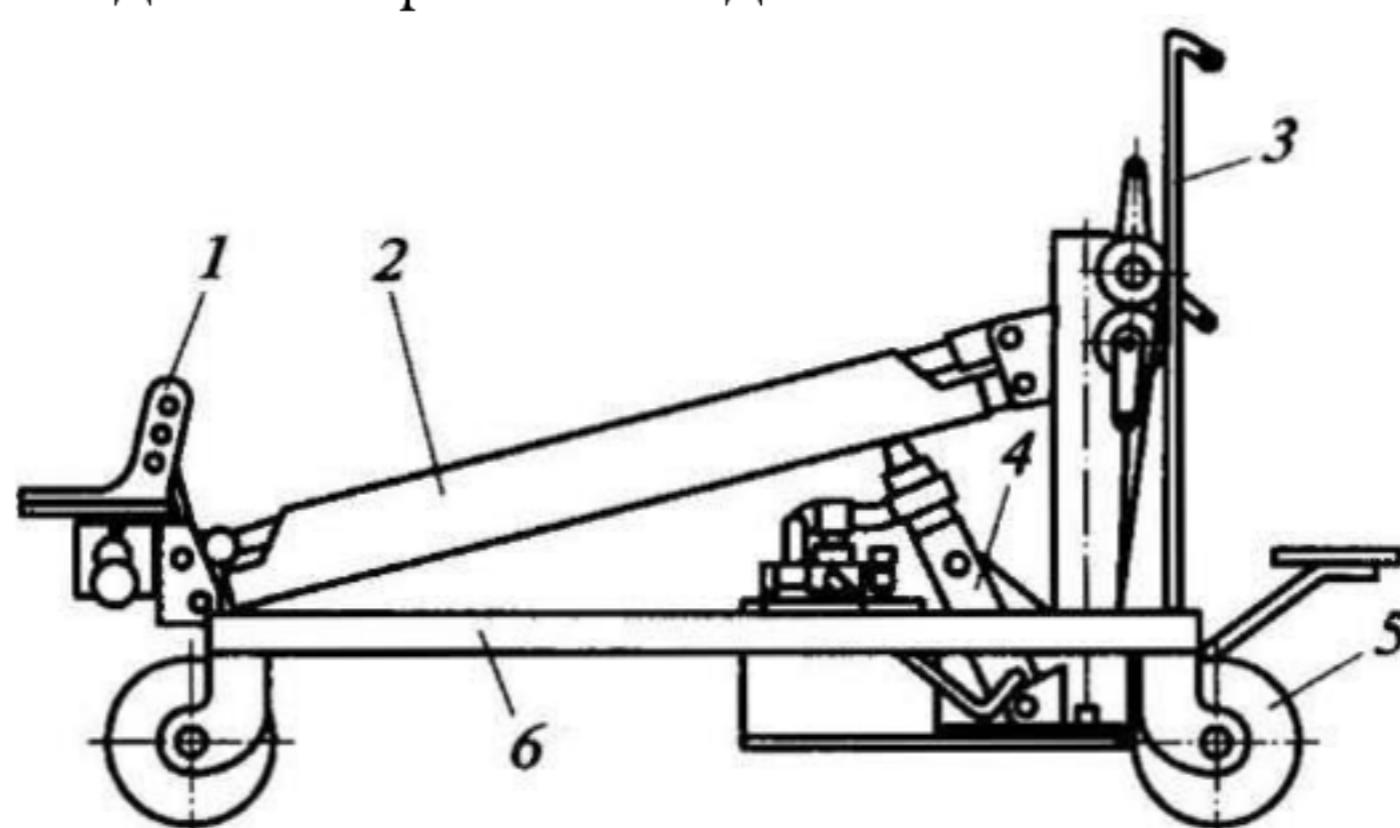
Техническая схема снятия и постановки рессор: 1 — подхват для рессор; 2 — стрела; 3 — гидроцилиндр; 4 — гидроцилиндр; 5 — колесо; 6 — щицольная балка
